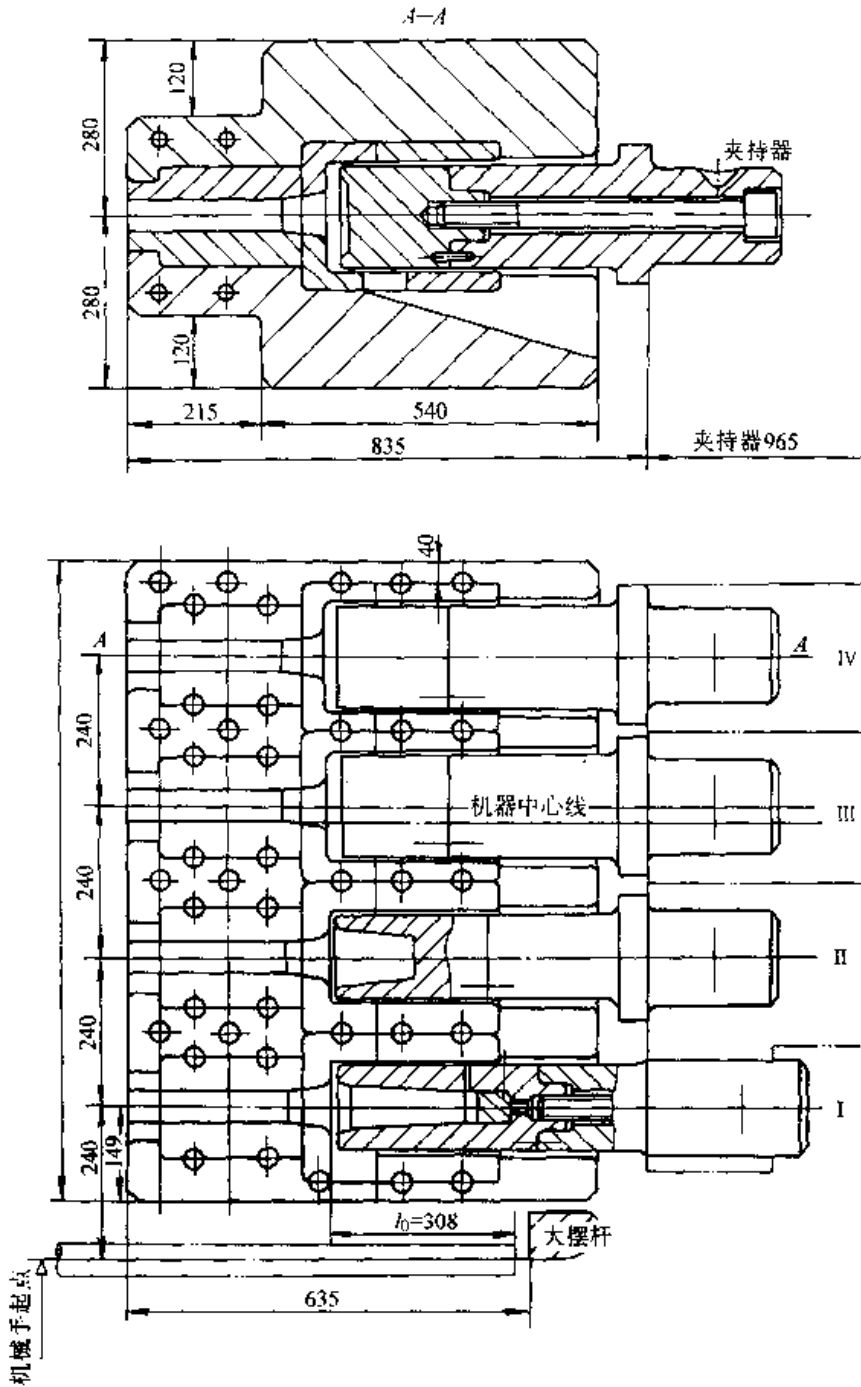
16 000 kN 平锻机半轴机械化模具图
